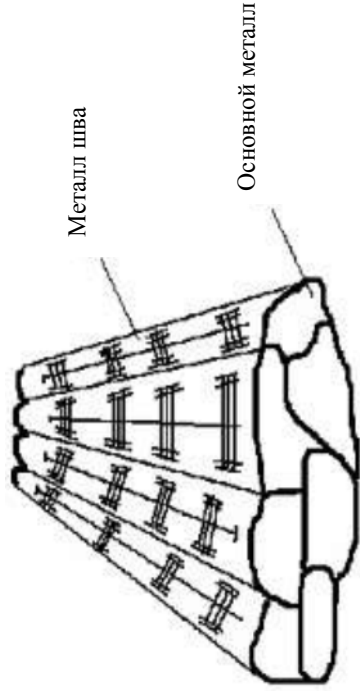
Схема роста кристаллов от границы сплавления в сварочной ванне
